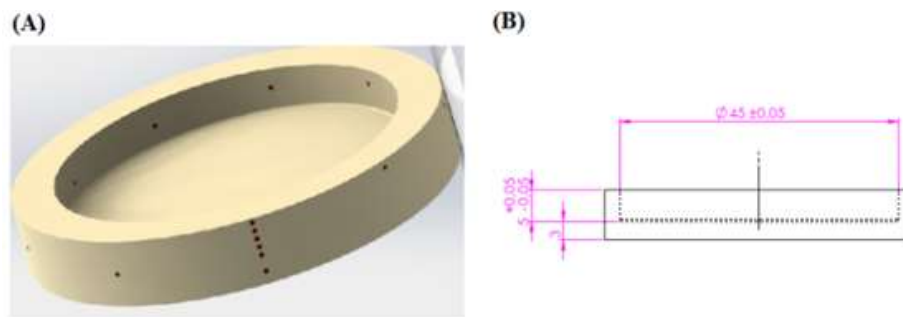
(A) Coupelle utilisée pour la mise en forme d'échantillon, (B) Dimensions de la coupelle
